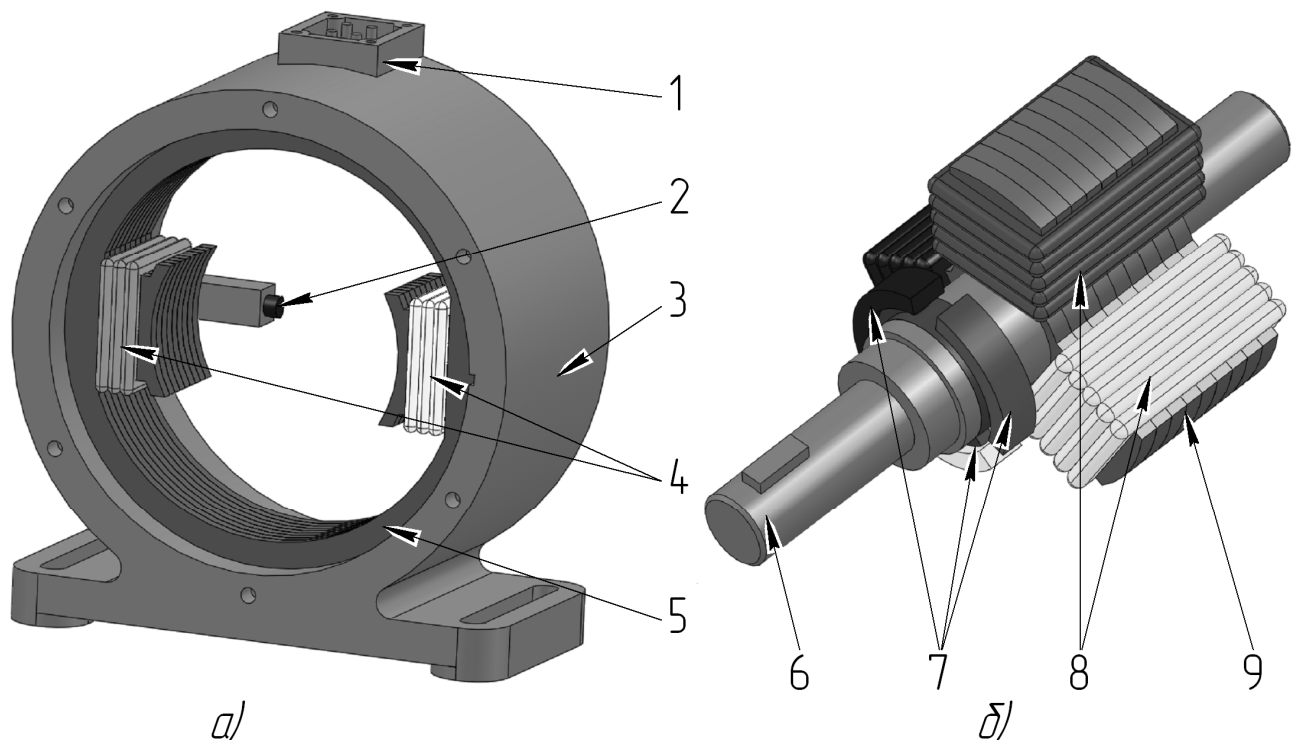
а) конструкция индуктора (а) и якоря (б): 1 – клеммник; 2 – щетки; 3 – станина; 4 – полюсные катушки индуктора; 5 – магнитопровод индуктора; 6 – вал; 7 – коллектор; 8 – сектора (обмотка) якоря; 9 – магнитопровод якоря
